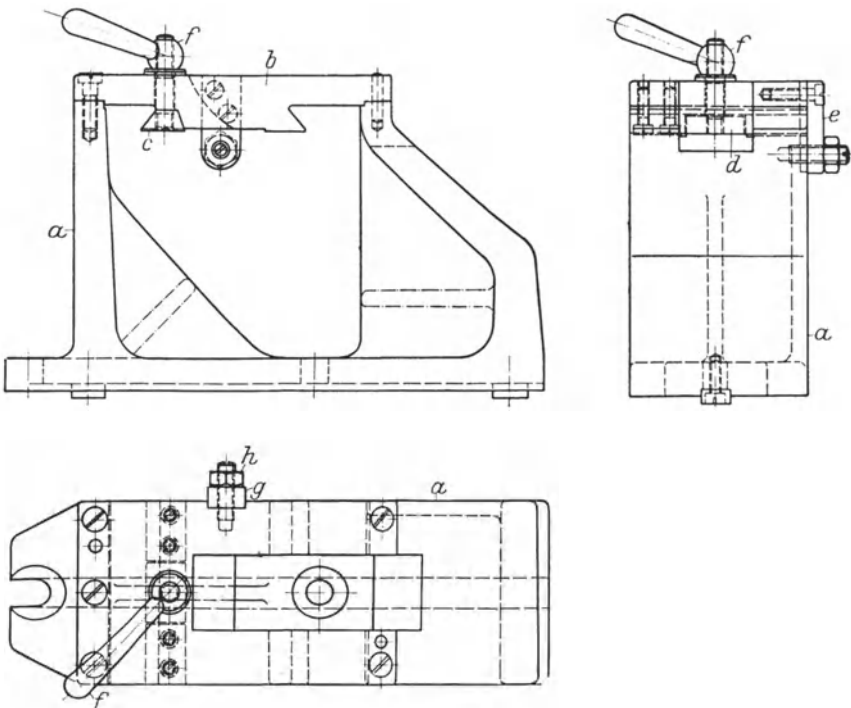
Aufspannvorrichtung zum Fräsen von Haltern für Pinolen.
